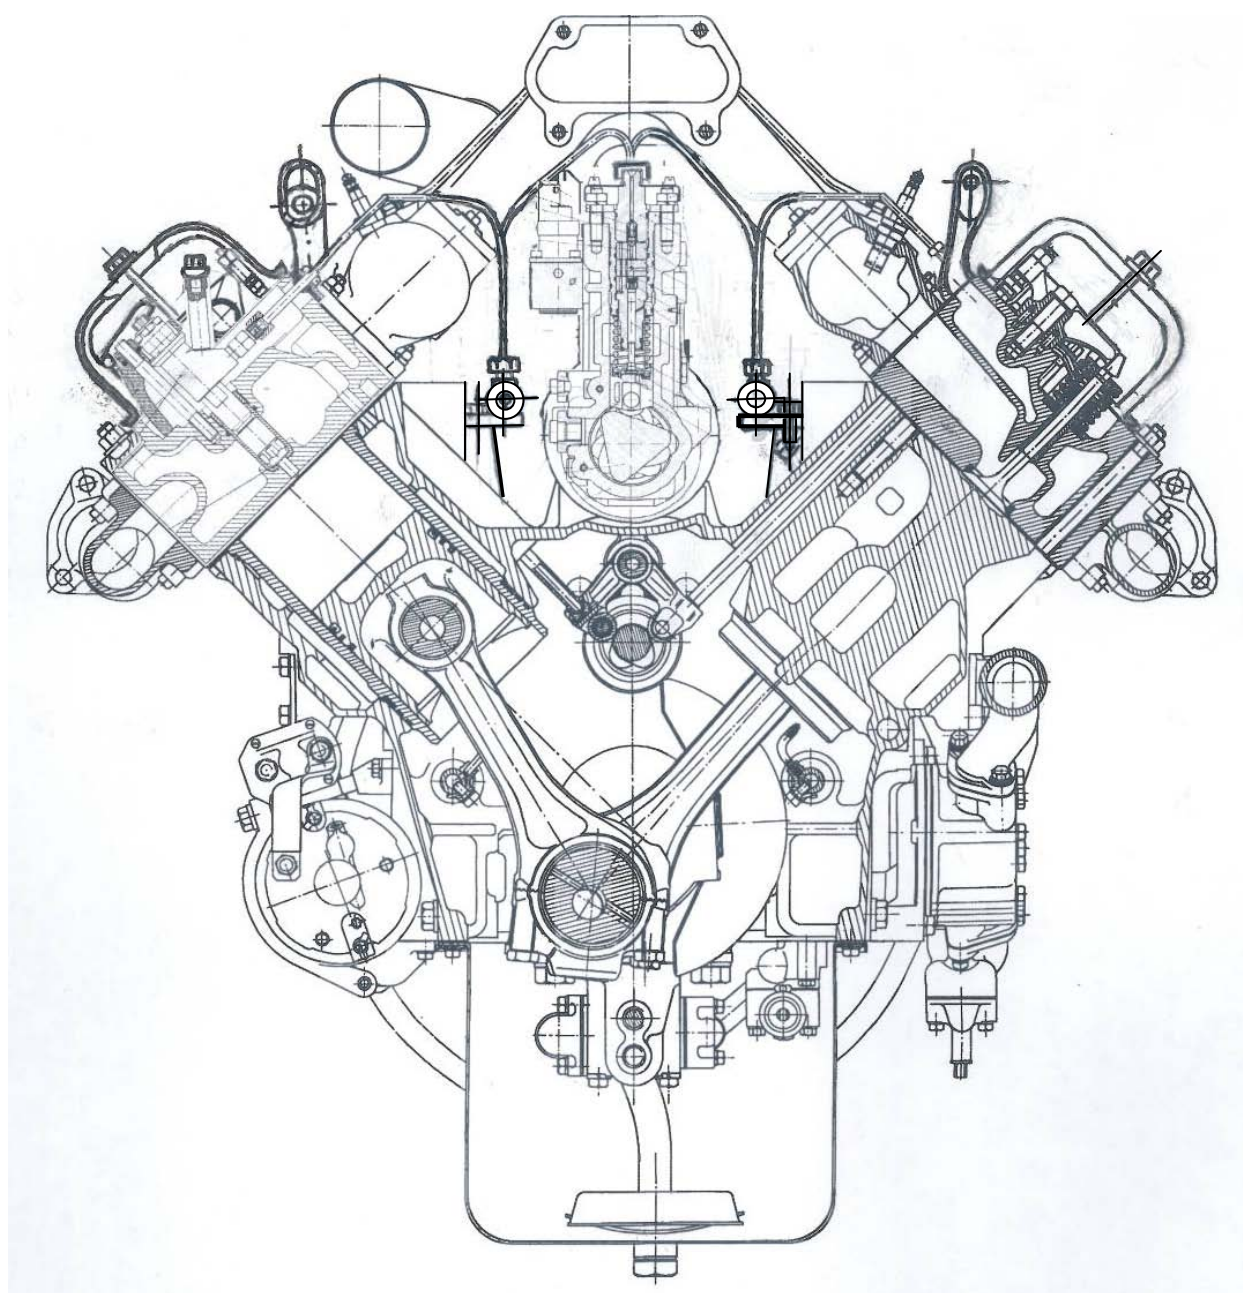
Поперечный разрез двигателя типа ЯМЗ-6565
